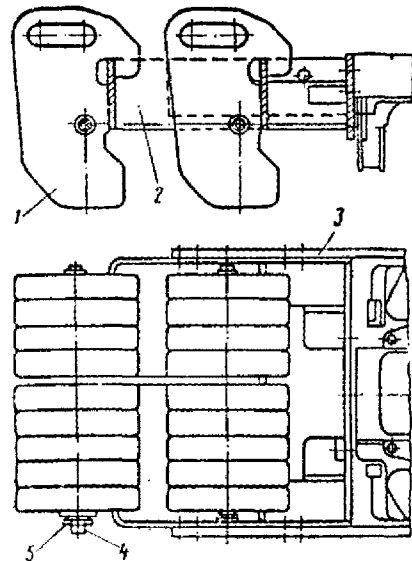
Установка передних балластных грузов на тракторы МТЗ: 1 – балластный груз; 2 – кронштейн; 3 – боковая пластина; 4 – струна; 5 – гайка
